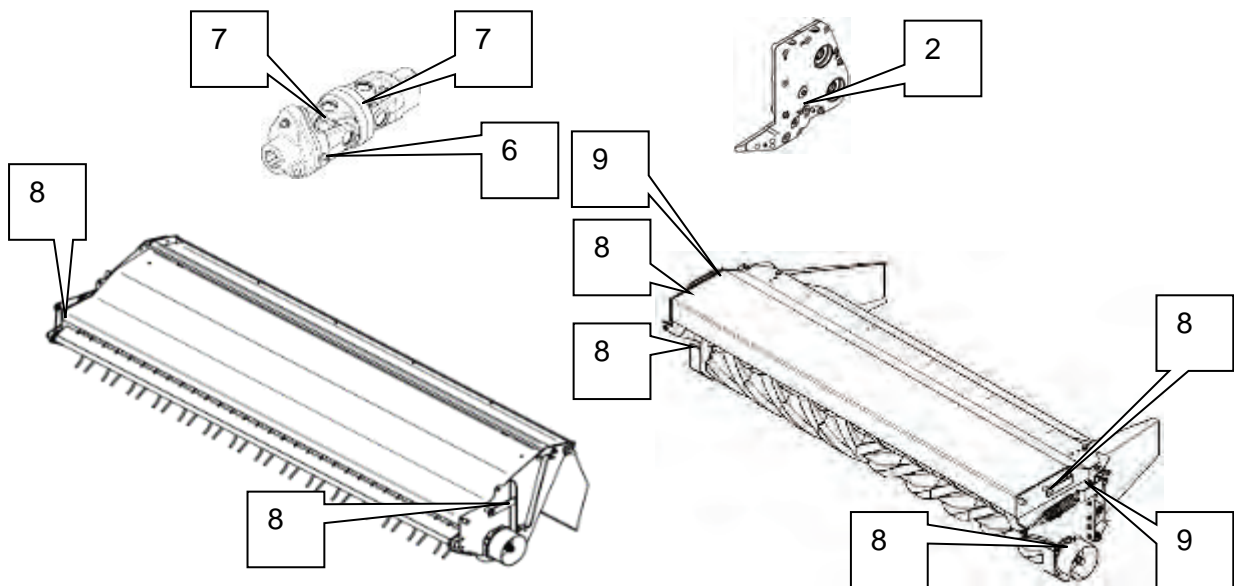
Puntos de lubricación en el acondicionador de púas (izquierda) o en el preparador de rodillos (en la parte derecha de la figura)
